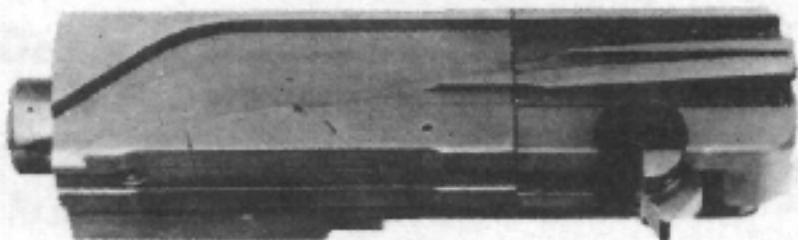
Ensemble mobile en position de fin de mouvement avant.
